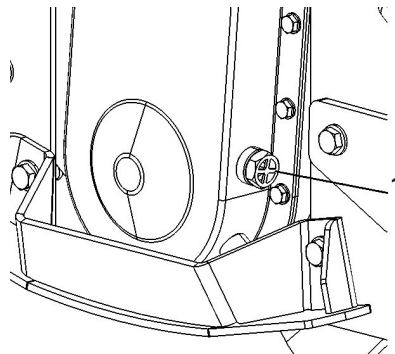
Ölstand im Kettengetriebe 1 – Kontrollschraube mit Schauglas
